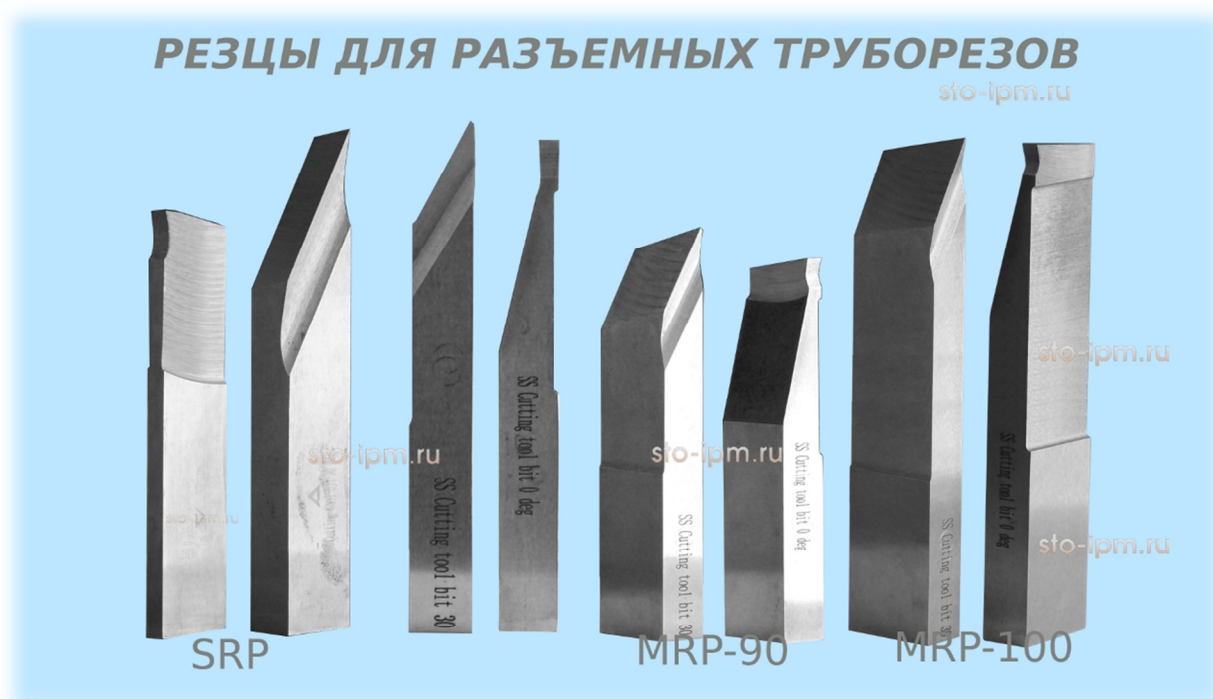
Резцы SRP и MRP для разъемного трубореза
